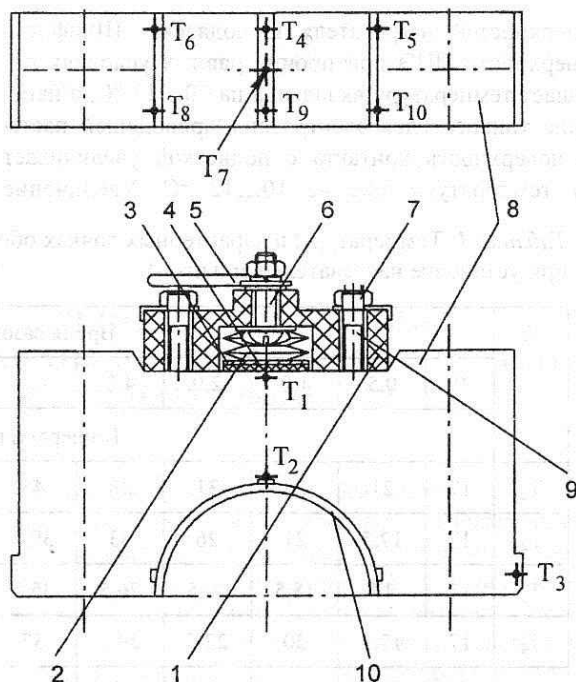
Схема установки термоэлектрических преобразователей ТХК на обогреваемой лабораторной подвеске КВ: 1 – электротеплоизоляционный корпус; 2 – тарельчатая пружина; 3 – подпружиненный контакт клеммы «+»; 4 – позисторный нагревательный элемент; 5 – токоподводящий провод; 6 – винт; 7 – стопорная шайба; 8 – подвеска; 9 – болт; 10 – вкладыш; $T_1 \dots T_{10}$ – места установки термопар
